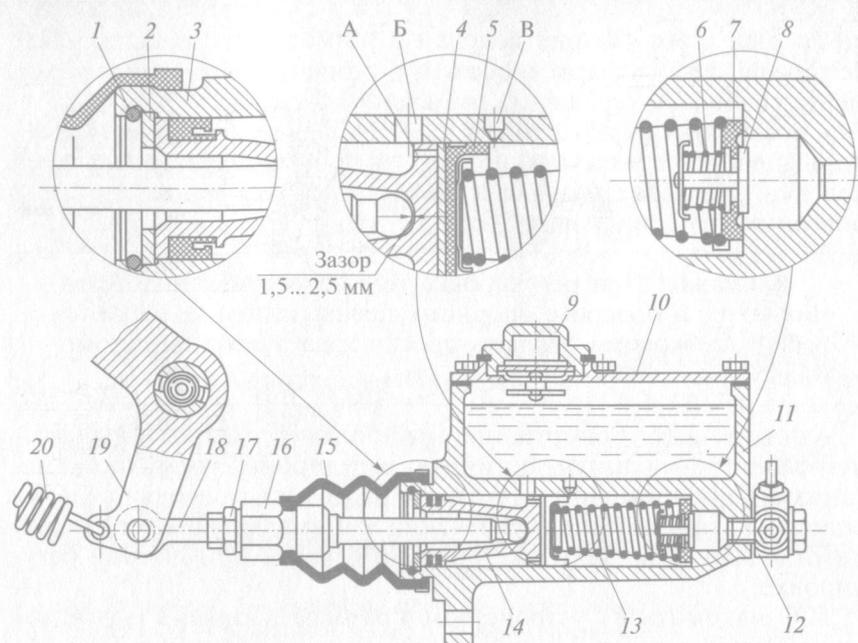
Главный тормозной цилиндр гидропривода тормозных механизмов автомобиля ГАЗ-53А:
